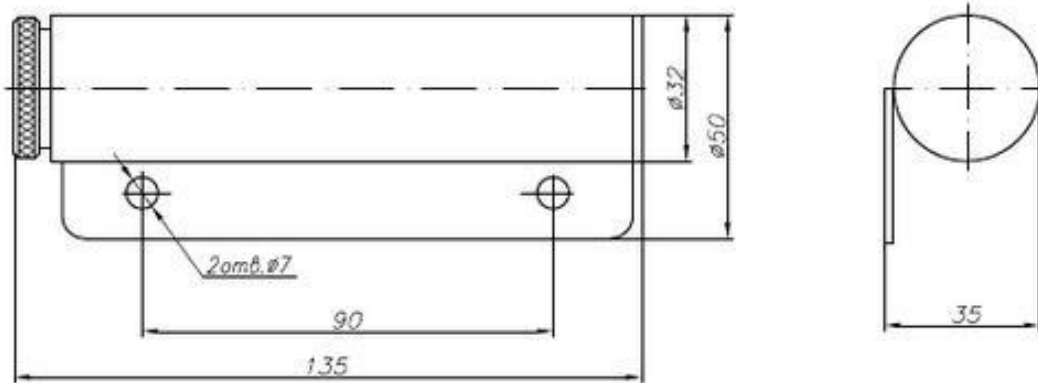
Габаритные и присоединительные размеры капсулы с магнитом.
